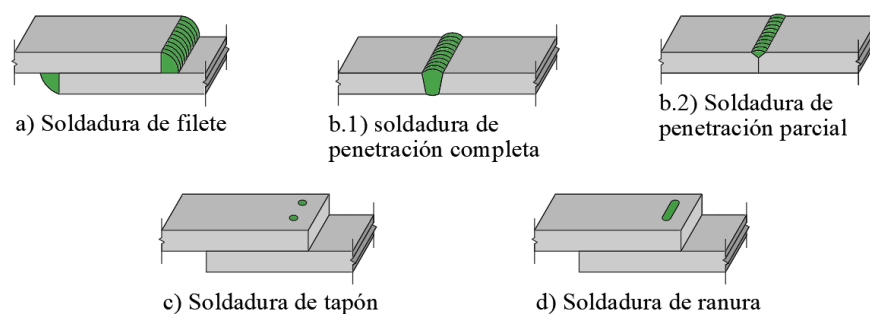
Tipos de soldaduras
